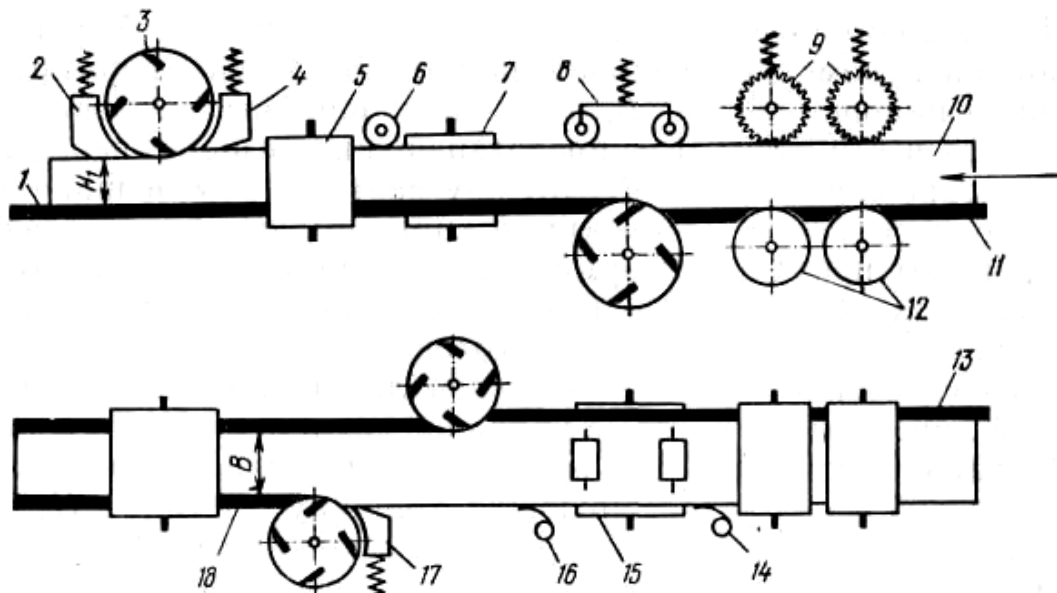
Схема четырехстороннего продольно-фрезерного станка: 1 — задняя часть стола, 2 — задний прижим, 3 — верхний горизонтальный вал, 4 — передний подпор, 5, 7 — фрезы, 6 — верхний прижим, 8 — роликовый прижим, 9 — верхние рифленые валцы, 10 — заготовка, 11 — передняя часть стола, 12 — нижние гладкие валцы, 13 — направляющая линейка, 14, 16 — боковые прижимы, 15 — нижний ножевой вал, 17 — прижим, 18 — левая направляющая линейка
